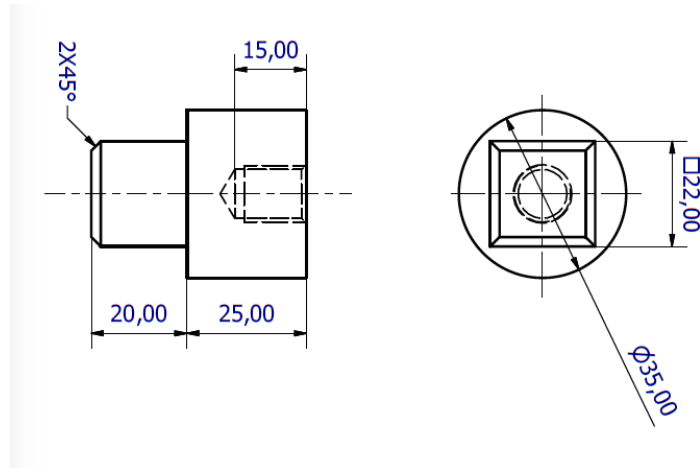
Projeto em CAD do corpo-de-prova
